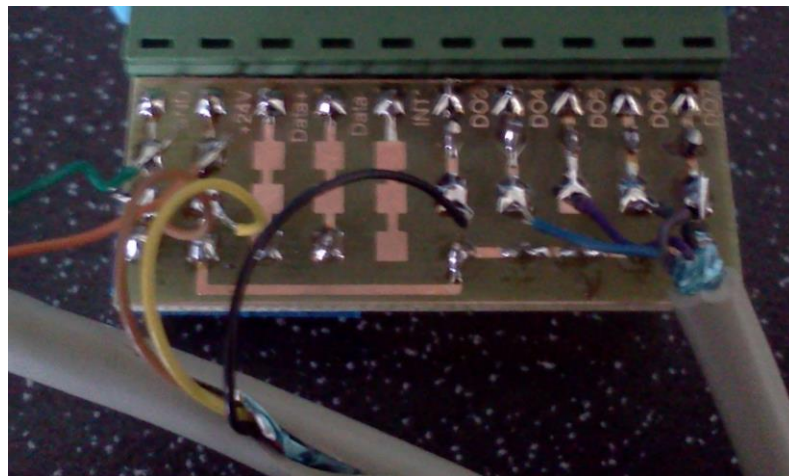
Detail plošného spoje na horní straně modulu ADAM (strana součástek)
